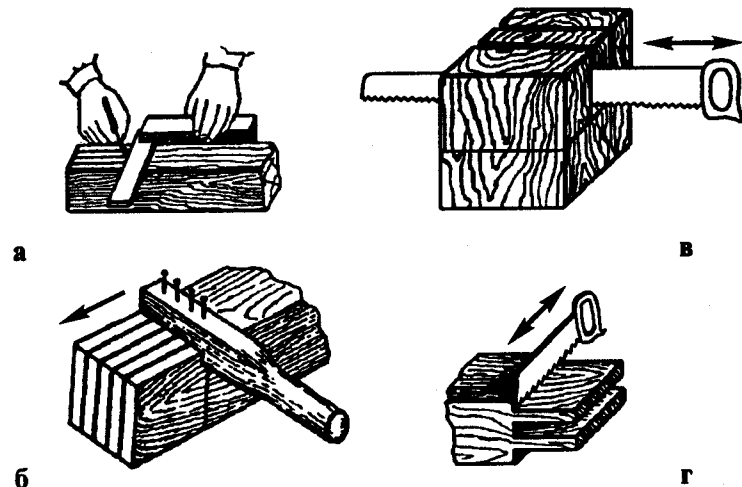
Последовательность изготовления шипового соединения: а — поперечная разметка; б — продольная разметка; в — продольное выпиливание шипа и проушины; г — поперечное выпиливание шипов
